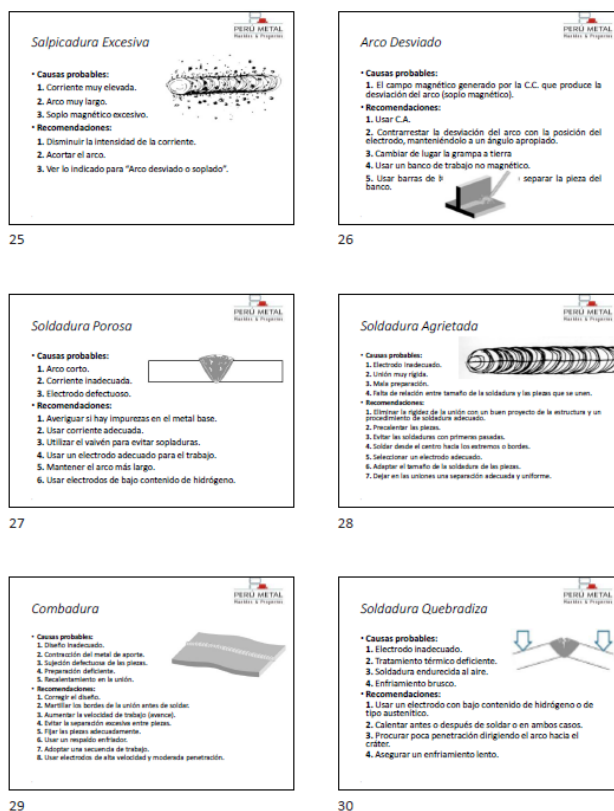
Láminas 25-30 de capacitación sobre técnicas de soldadura
